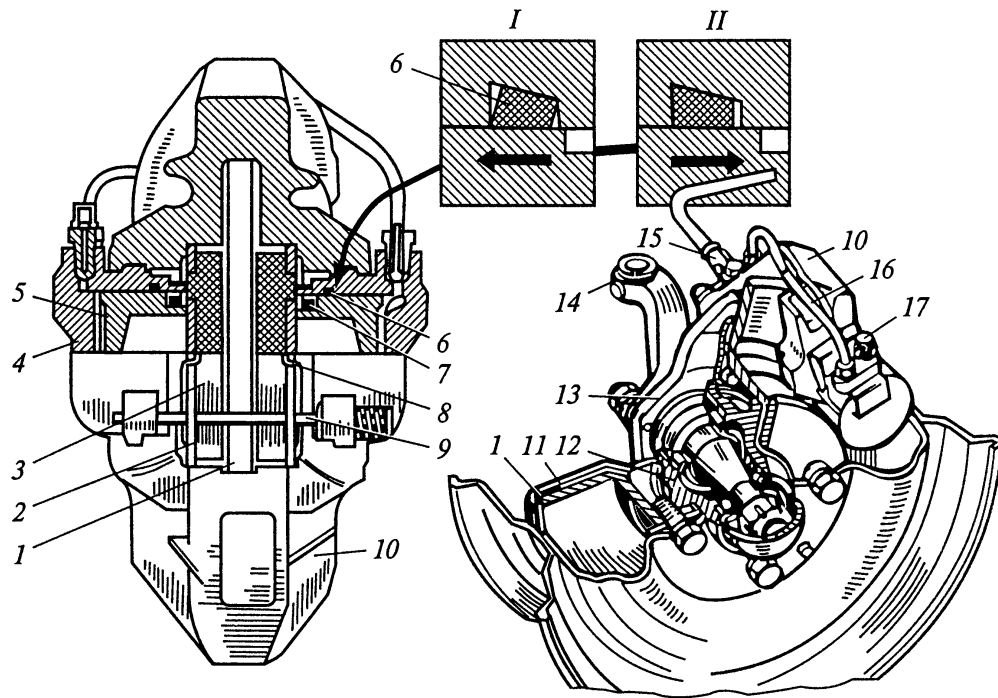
Передній гальмівний механізм задньоприводного легкового автомобіля: 1 – гальмівний диск; 2 – колодка; 3 – накладка; 4 – циліндр; 5 – поршень; 6 – кільце; 7 – ковпачок; 8 – пружина; 9 – палець; 10 – супорт; 11 – щит; 12 – маточина; 13 – кронштейн; 14 – поворотний кулак; 15, 17 – штуцери; 16 – трубка
